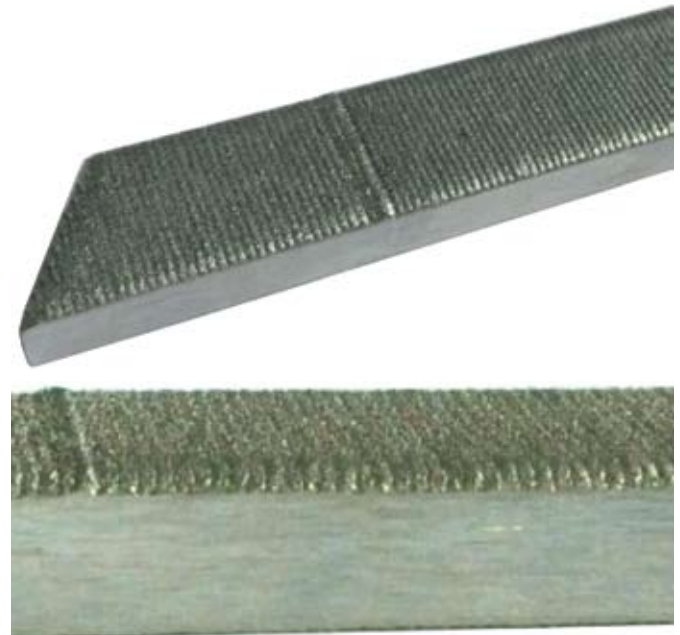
Общий вид покрытия, полученного при лазерной наплавке
